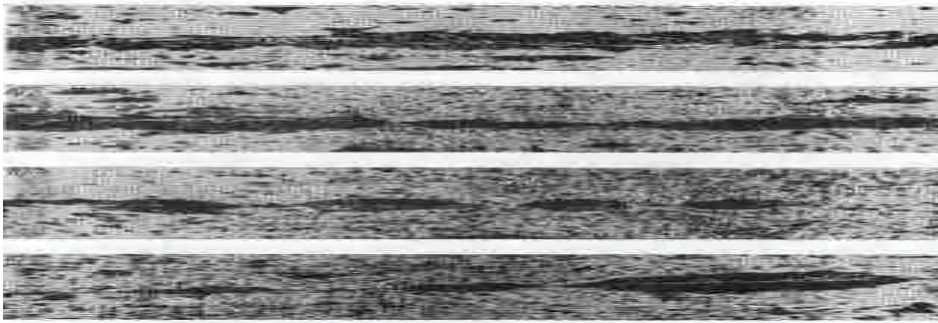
Образование сварного соединения при прокатке биметалла алюминий-сплав АО10-1
